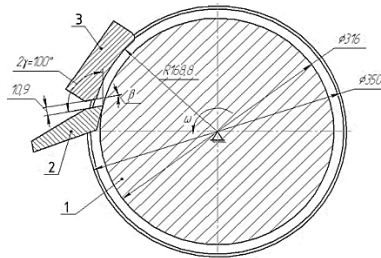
Схема инструмента для прессования заготовок прямоугольного сечения: 1 – ротор; 2 – упор; 3 – прижим
